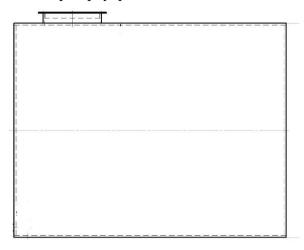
Эскиз резервуара РГС-10 зав.№ 37
